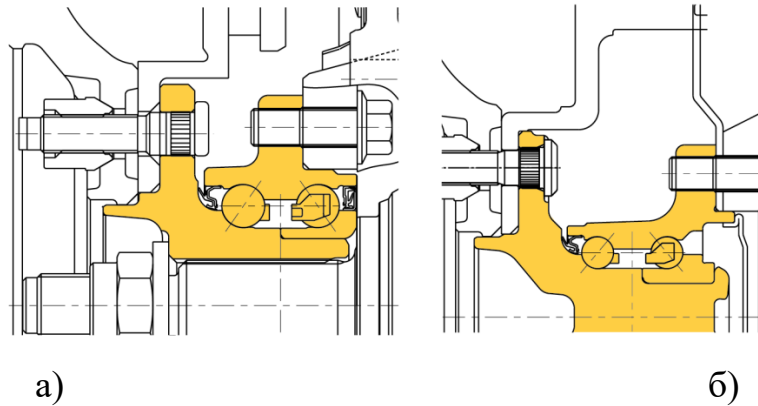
Ступичные подшипники 3E (а) и 3EW (б) типов
